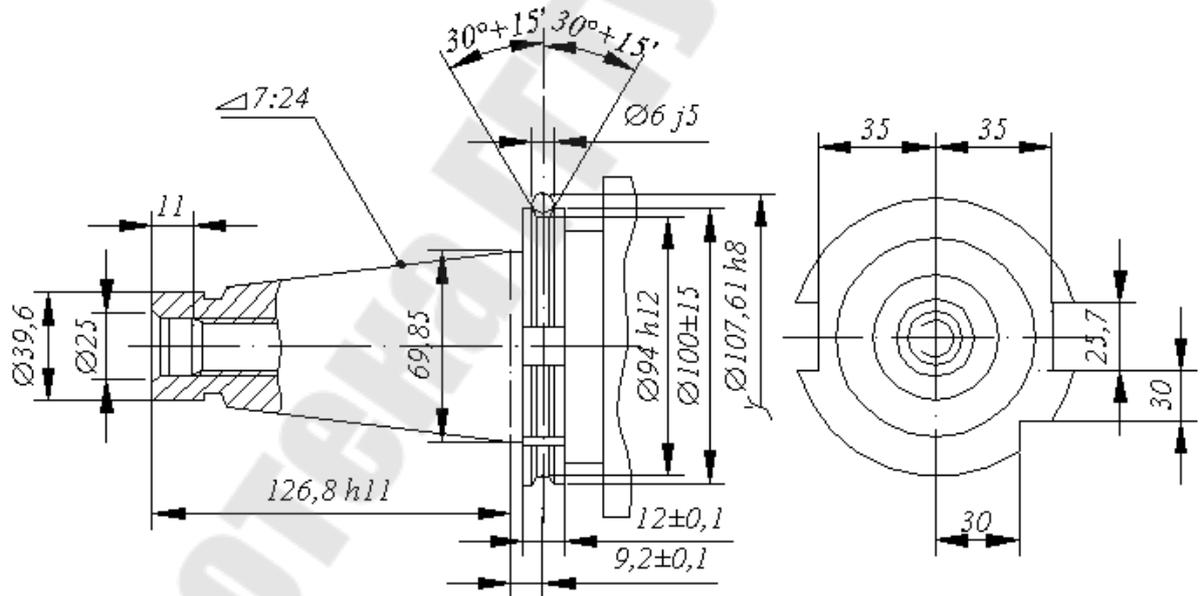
Инструментальные оправки с конусом 7:24 для автоматической смены инструмента в сверлильно-фрезерно-расточных станках.
